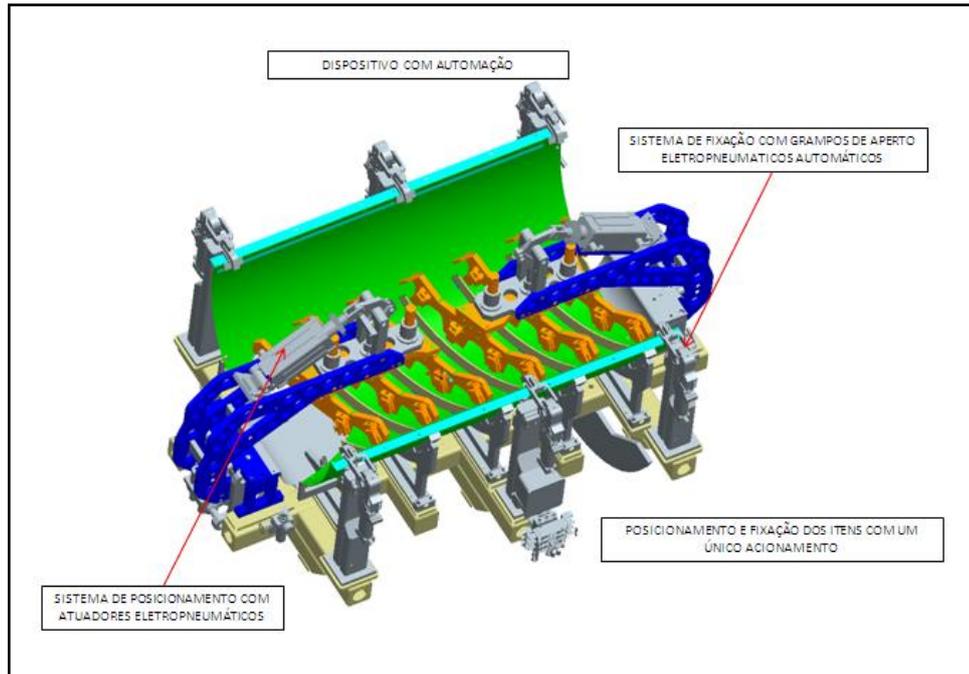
Dispositivo de solda com automação. Fonte: Pesquisa (2012)
